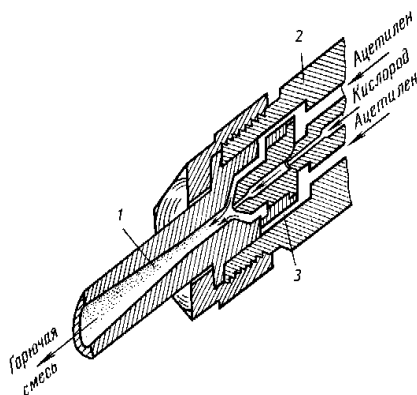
Инжекторное устройство, где 1 – смесительная камера, 2 – инжектор, 3 – корпус горелки
